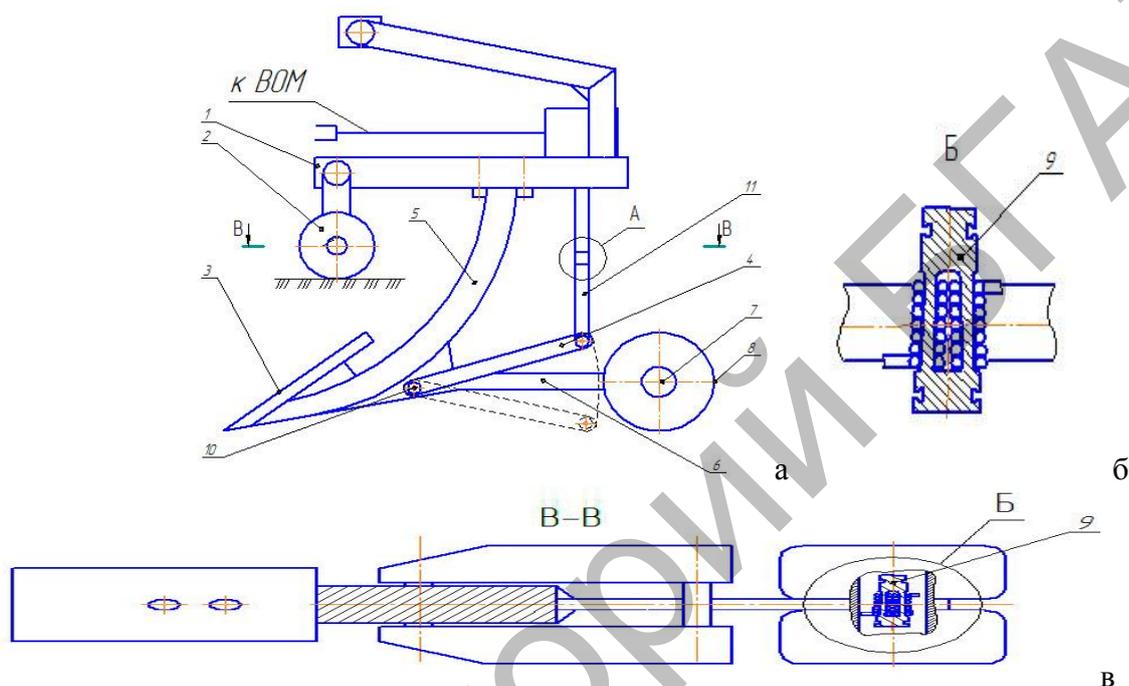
Схема устройства для осуществления способа накопления талых вод (а – вид сбоку устройства, б – разрез Б, в – вид сверху):
